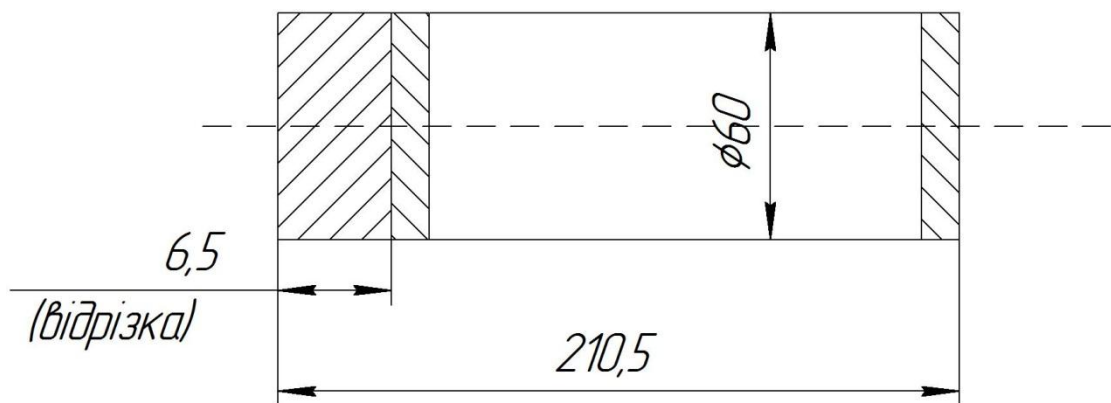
Ескіз штучної заготовки з круглого прокату
